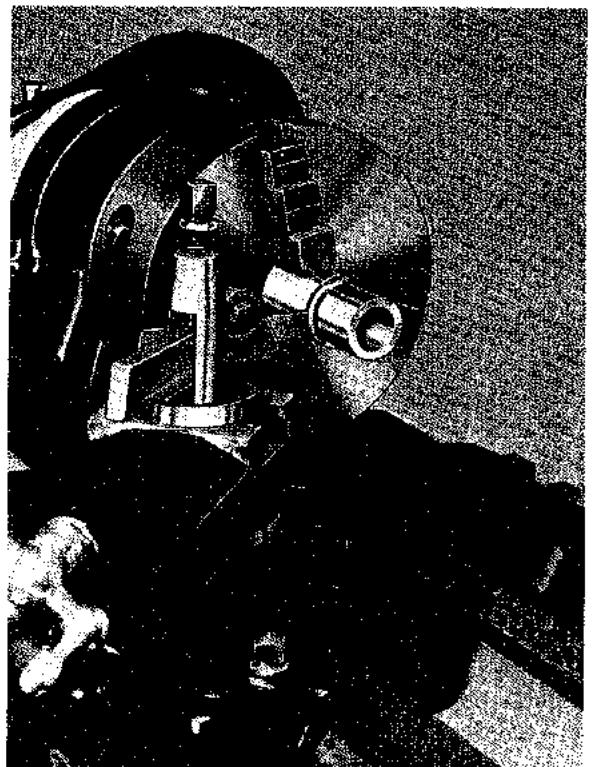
Tronzado de una pieza después del mecanizado (South Bend Lathe Works).
